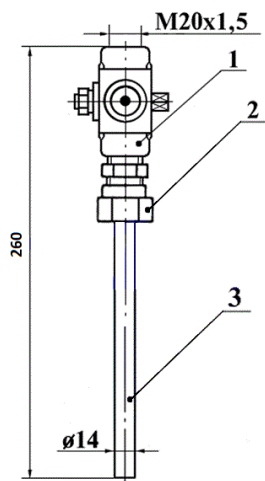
Закладная конструкция ЗК14-2-1-02
